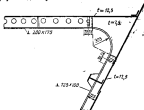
Сварная конструкция соединения бимса со шпангоутом.
